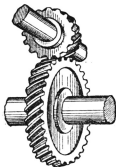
Винтовые цилиндрические зубчатые колеса.
